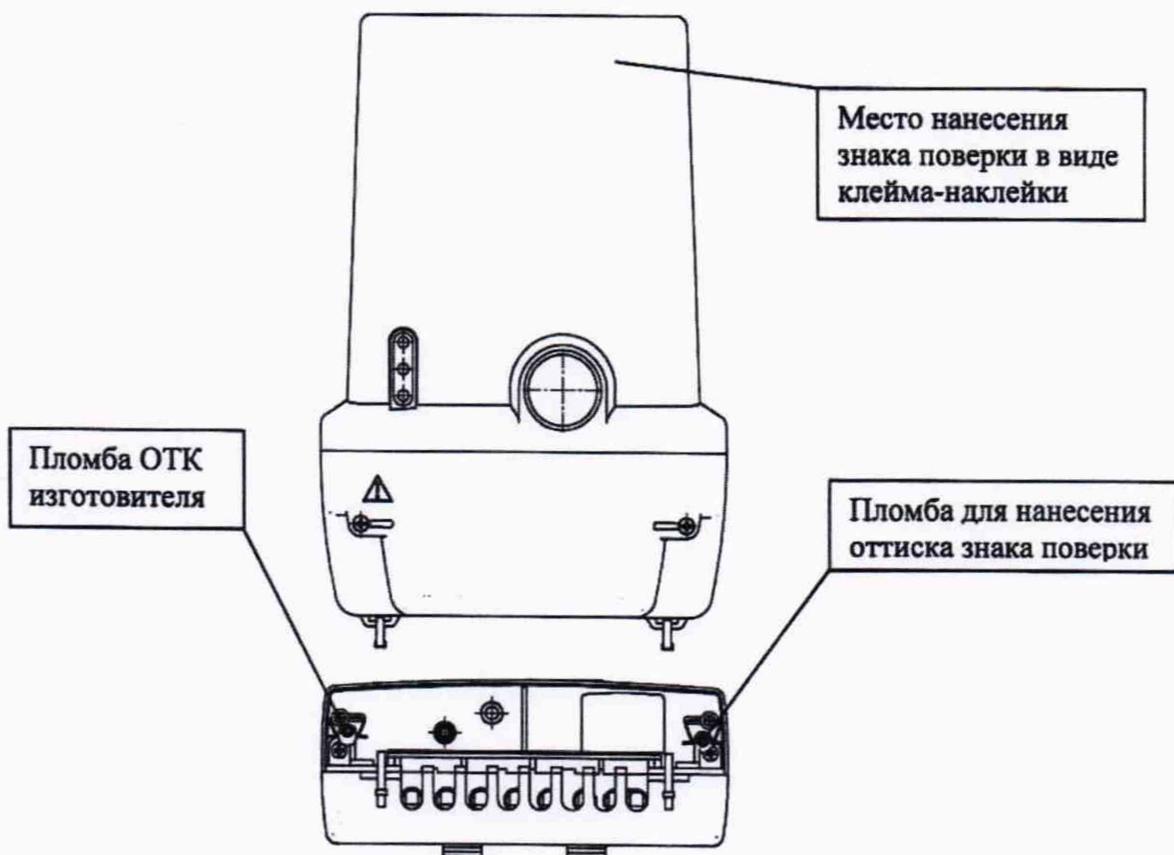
Вид корпуса счетчика СЕ318ВУ С3
